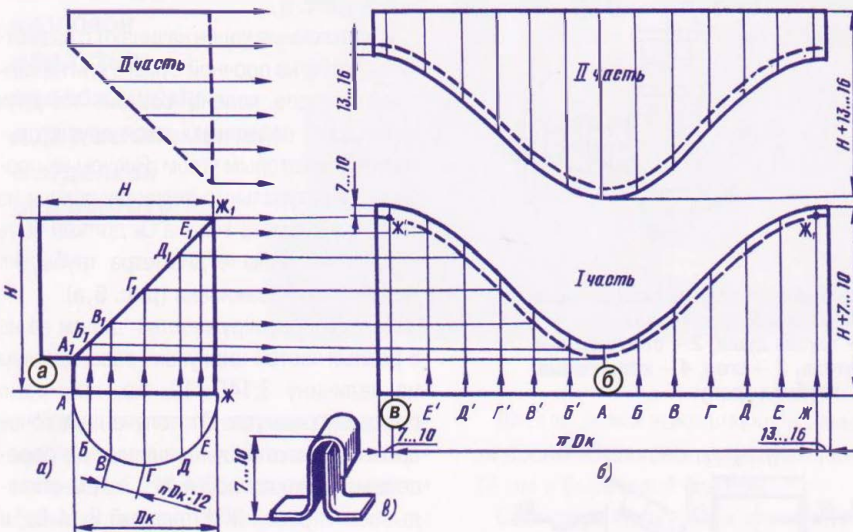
Изготовление колена: а — проекция колена, б — развёртки заготовок колена, в — отгиб кромок и соединение их в одинарный стоячий фальц.
